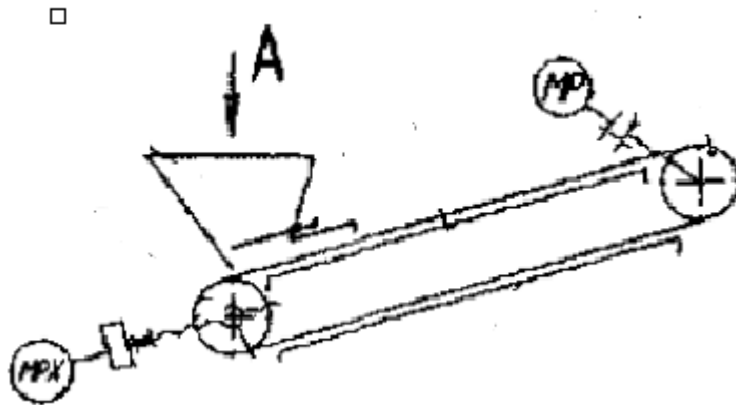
схема конвеєра з пристроєм для автоматичного регулювання натягу стрічки та усунування сходження її з барабана
